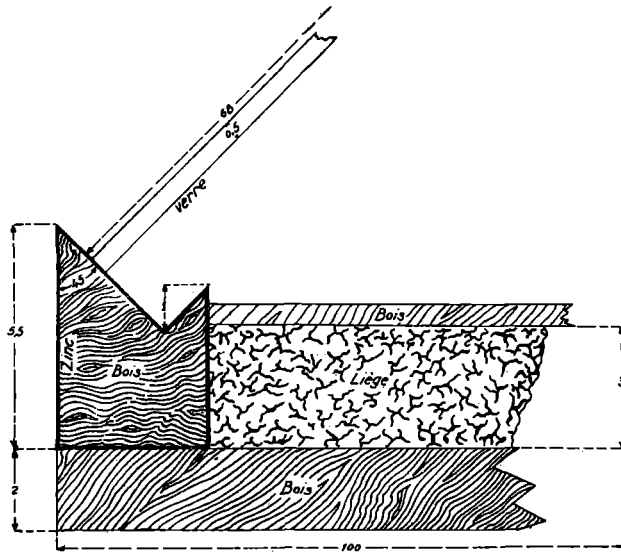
Appareil de type I, variante 2: schéma de construction.
